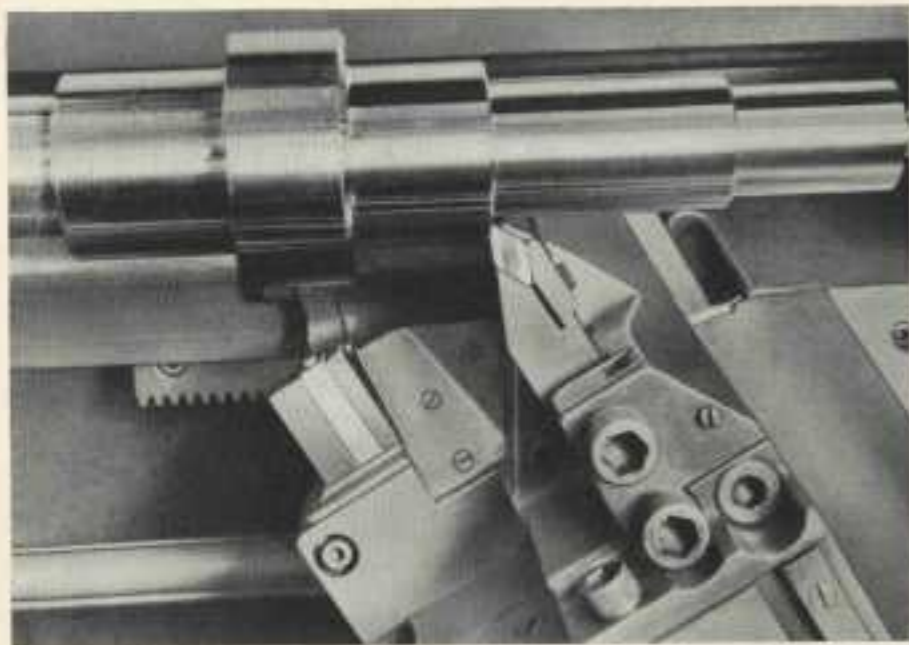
Il nuovo tipo di utensile montato sulla macchina.
